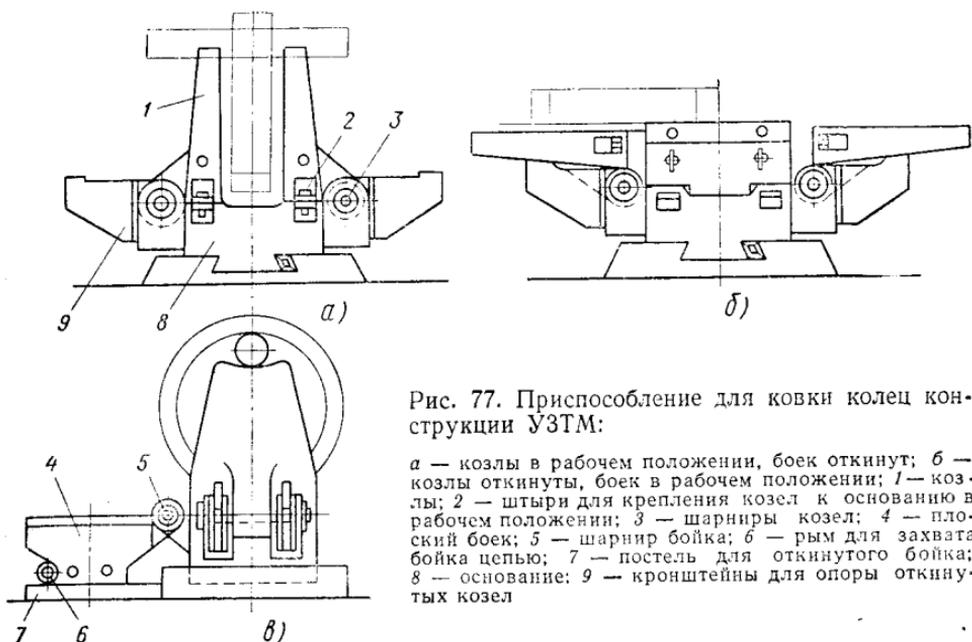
Приспособление для ковки колец конструкции УЗТМ:
